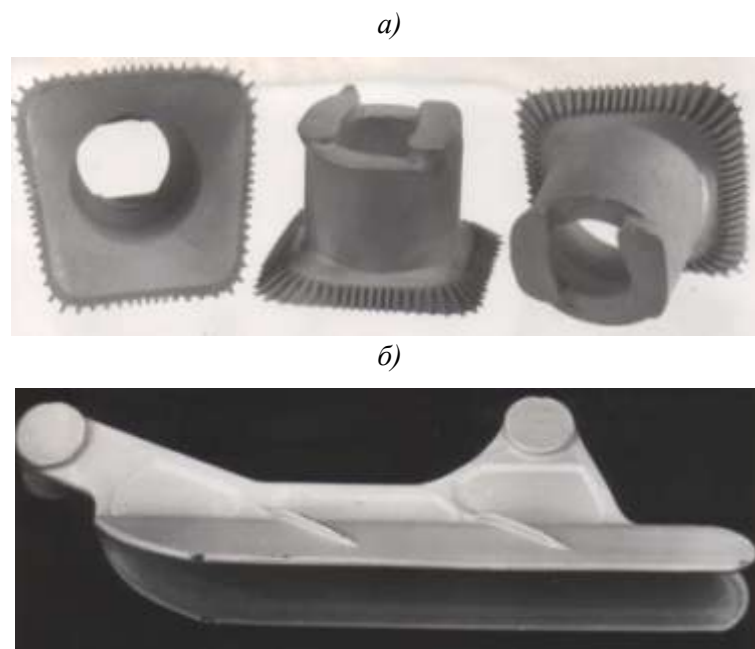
Отливки деталей из сплава ВКНА-1ЛКВИ, а) диффузор; б) стойка сопла
